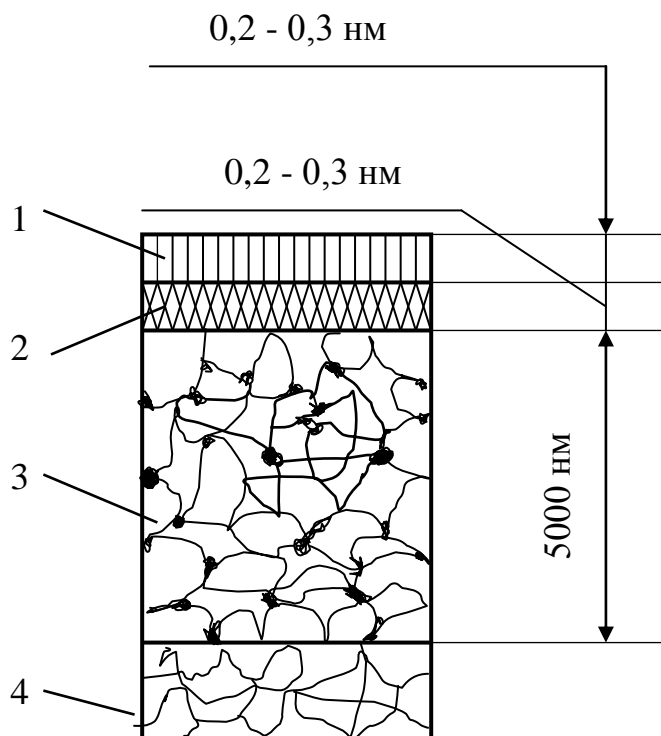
Структура поверхнього шару шліфованої деталі з вуглецевої сталі
